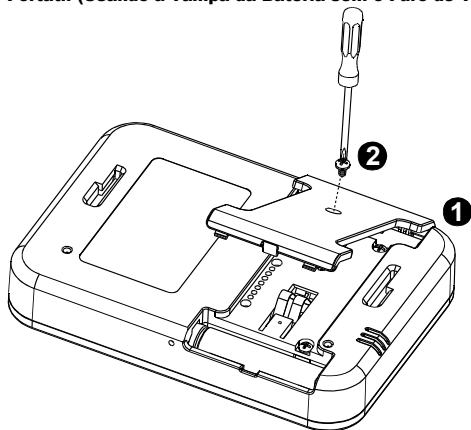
Montagem da Tampa da Bateria (Parte a)
